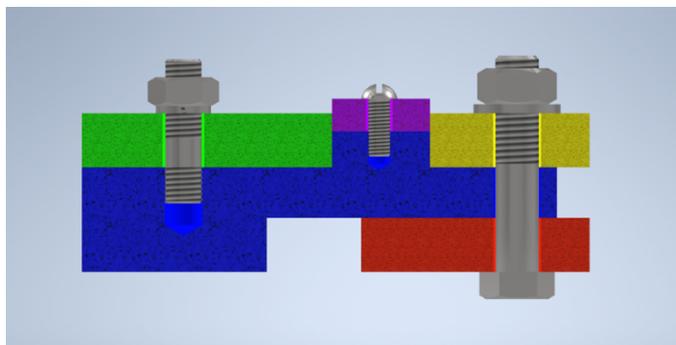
3D-модель сборочного узла со стандартными компонентами крепежных деталей
